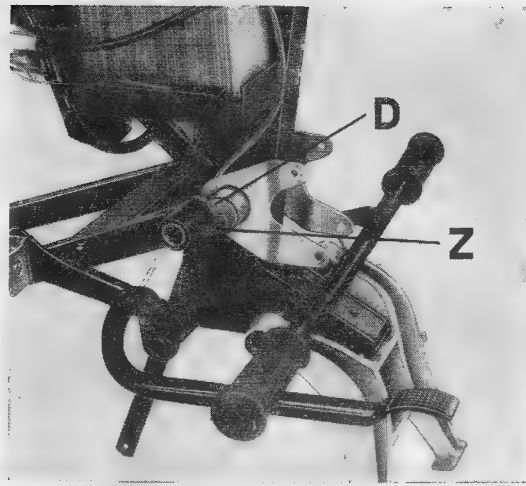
Motorschuhe durch Druckring (D) und Zugspindel (Z) mit Gewinde M 6 axial zusammengedrückt, Hinterradschwinge aufgeschoben
